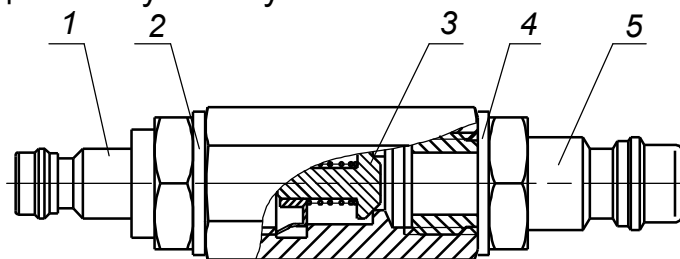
Приспособление Пр-652 для проверки давления на выходе редуктора
